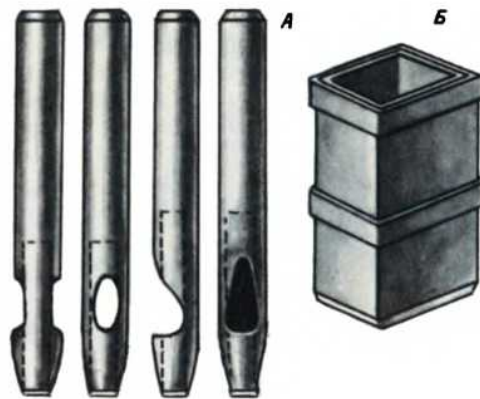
Пробойники для высечки отверстий: А — круглых; Б — квадратных.
